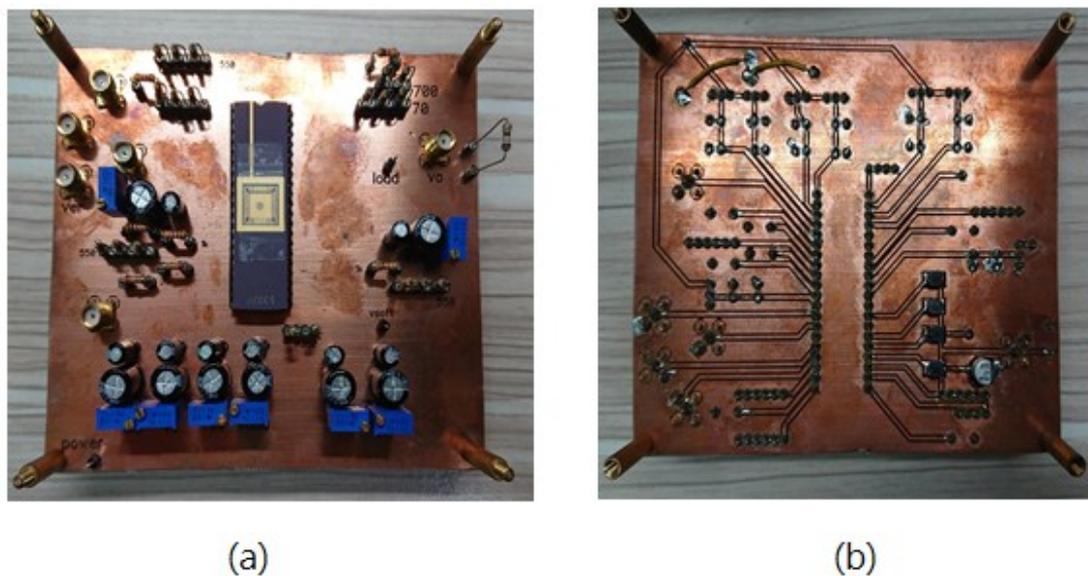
PCB 板正反面照相圖(a)為正面(b)為反面
